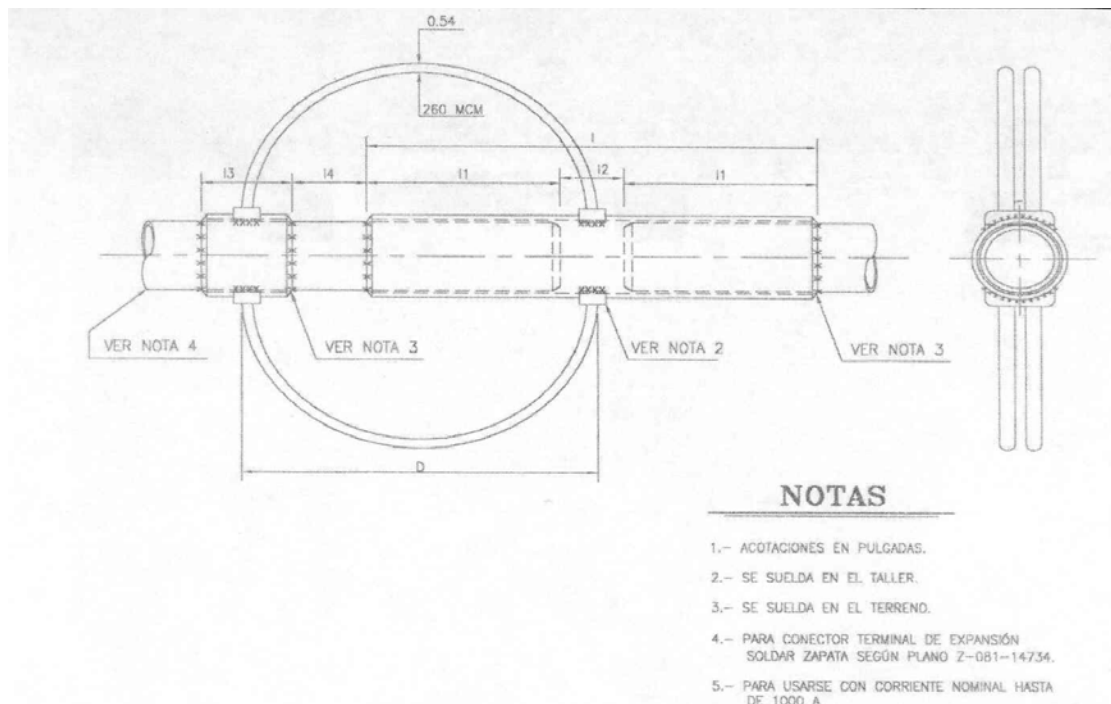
Cople de expansión diseñado y fabricado por LFC
